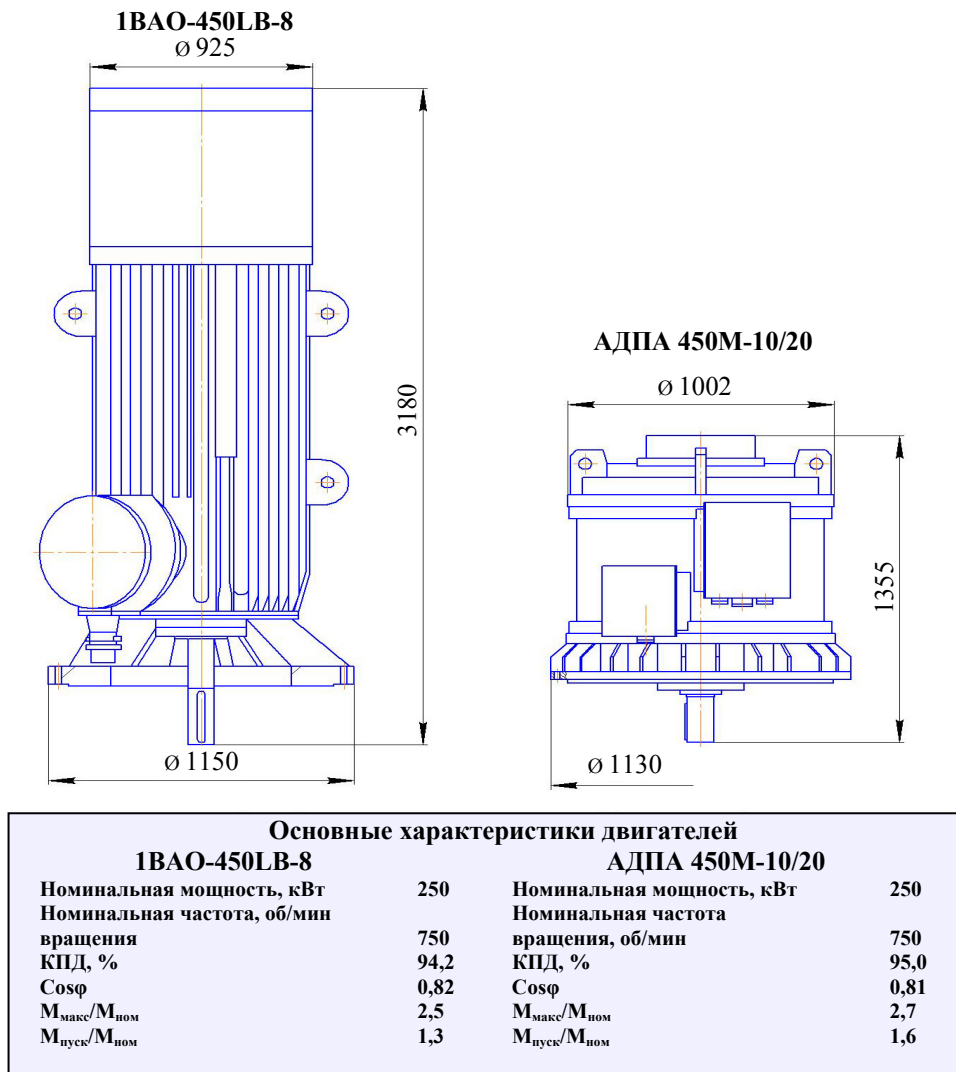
Габаритные размеры общепромышленного двигателя и АДПА 450
